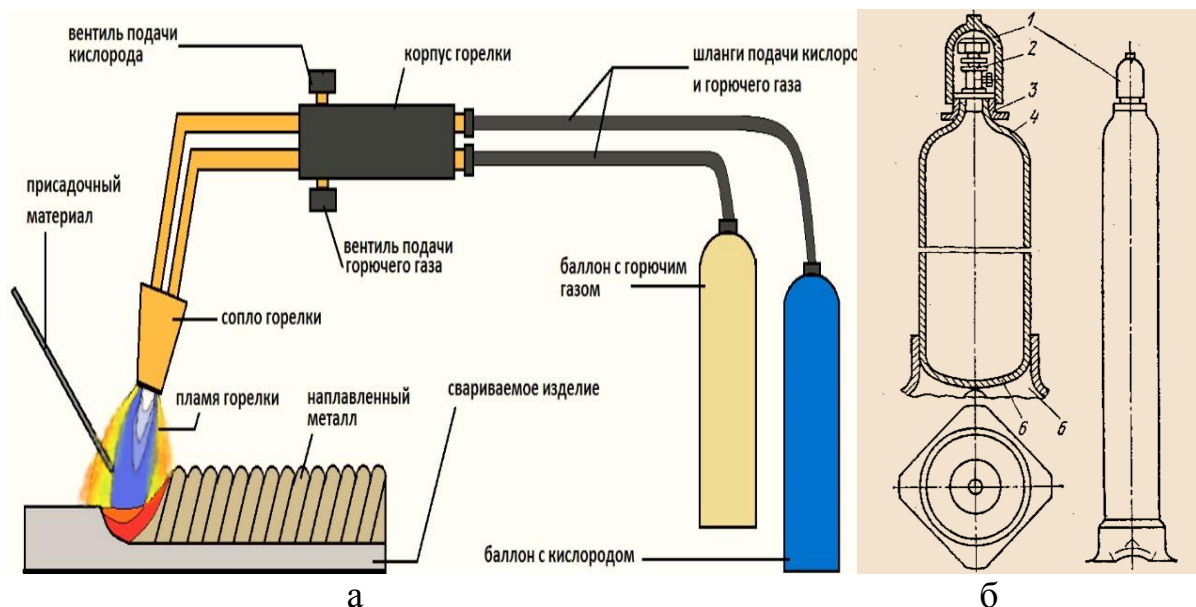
23. Схема газовой сварки (а) и схема газового баллона (б)
